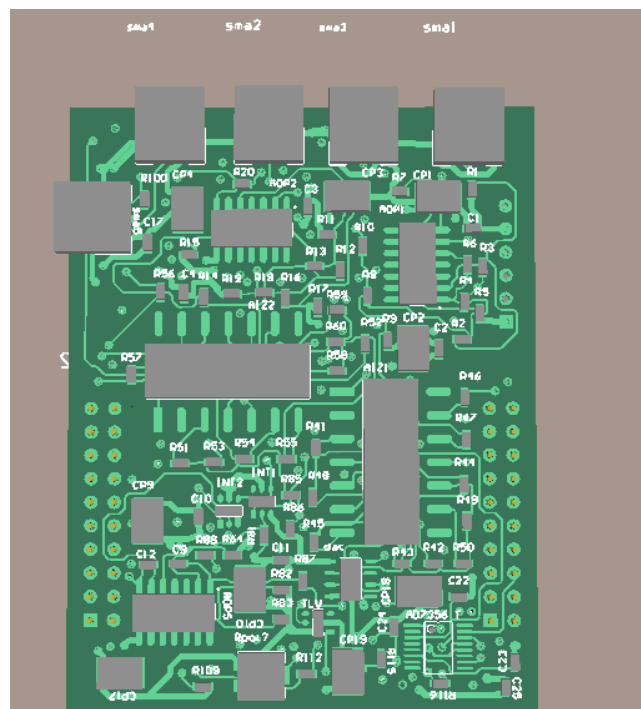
29 Vista en antiplanta de la placa desarrollada.
